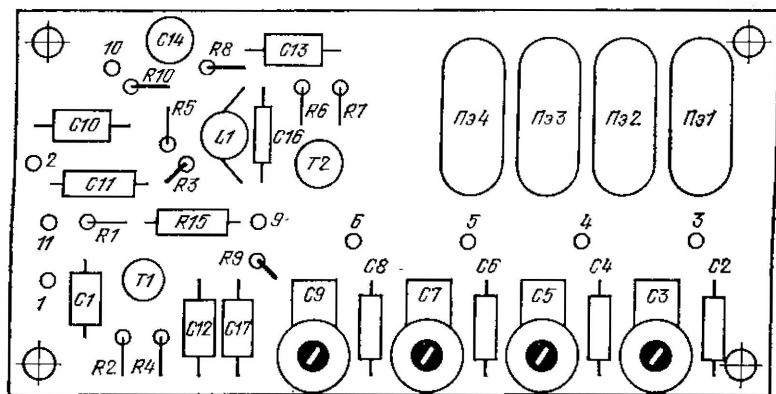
Монтажная схема деталей платы первого преобразователя частоты (вид сверху)
